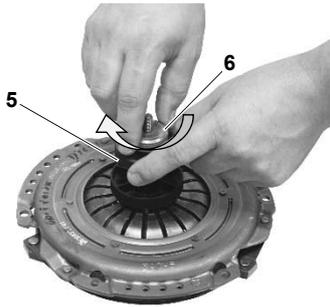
Serrer légèrement l'écrou de blocage sur la plaque de pression.
